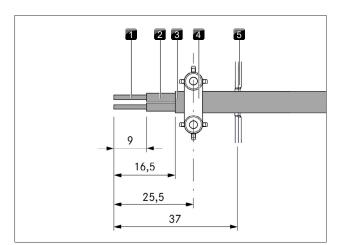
Comprimentos de decapagem e posição de montagem do cabo de ligação PKAS3/PKAS3AB - Home-Out
